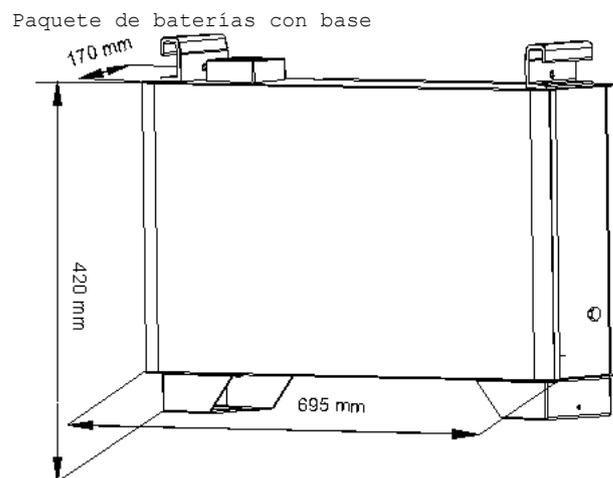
Dimensiones del paquete de batería BU3 tipo B con base
